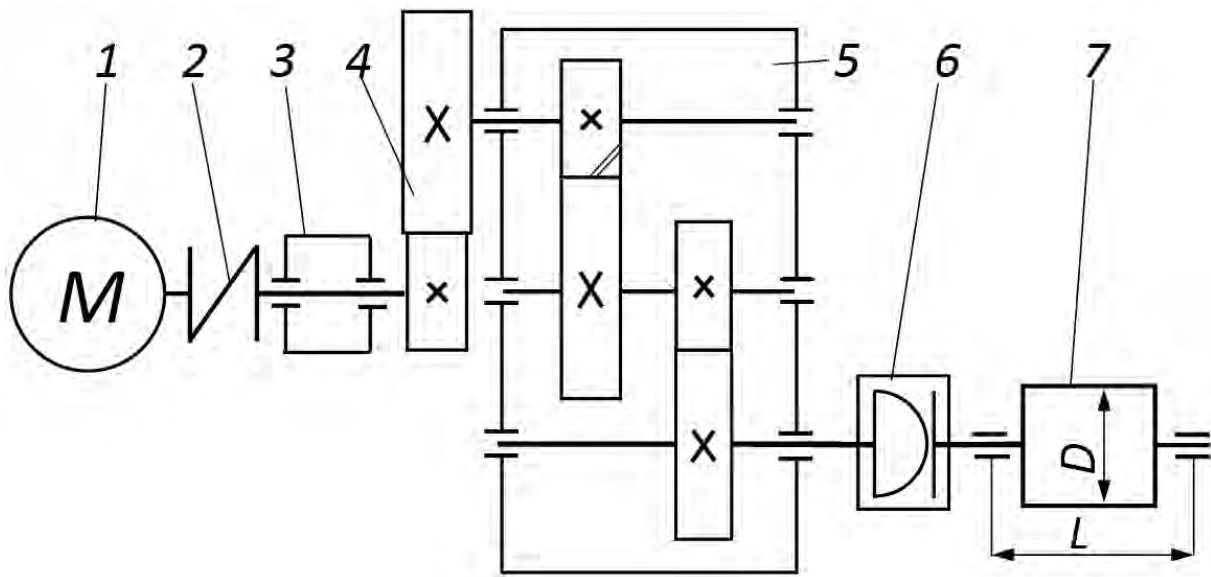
Схема привода ленточного конвейера (вид сверху): 1 – асинхронный электродвигатель; 2 – муфта упругая втулочно-пальцевая; 3 – первичный вал (вал на радиальных подшипниках качения установлен в сборной опоре (стакане)); 4 – открытая цилиндрическая прямозубая передача; 5 – редуктор цилиндрический двухступенчатый с косозубой и прямозубой передачами; 6 – муфта зубчатая; 7 – приводной вал с барабаном
